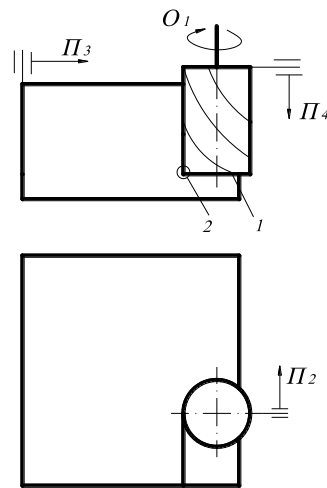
Схема фрезерування уступа кінцевою фрезою
